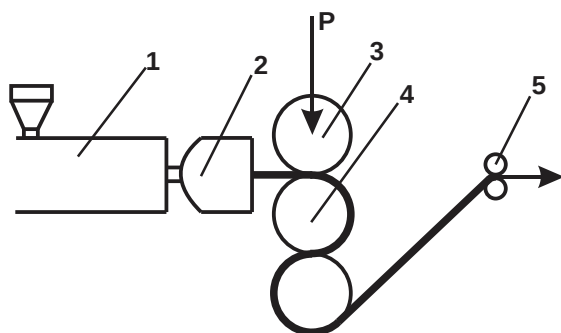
Instalație de extrudare a foilor: 1 – extruder; 2 – cap de extrudare; 3 – cilindru de presare; 4 – cilindri de finisare-răcire; 5 – cilindri de tragere.
